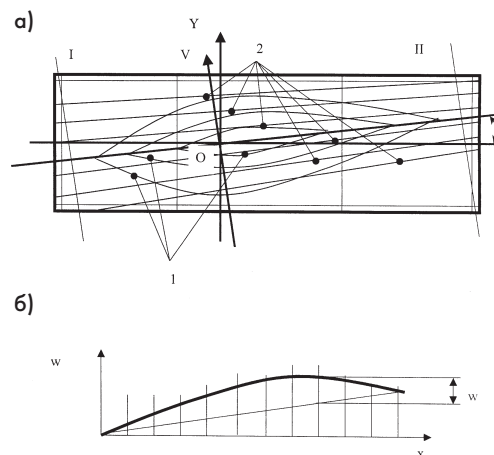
Разметка листовой заготовки для выполнения ротационно-локального формообразования: а — листовая заготовка в плане; б — сечение листовой детали (I, II);
